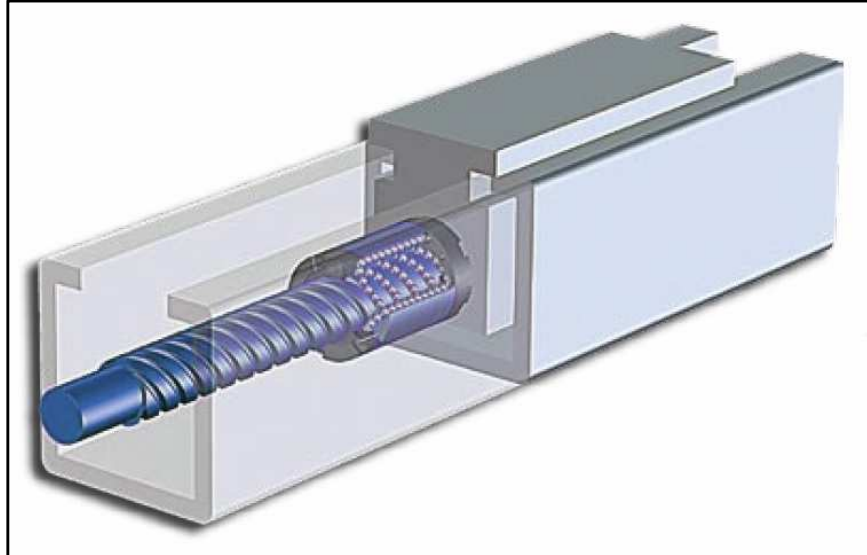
Vista de detalle de la unidad lineal Movopart con transmisión por husillos de bolas y guía deslizante.
